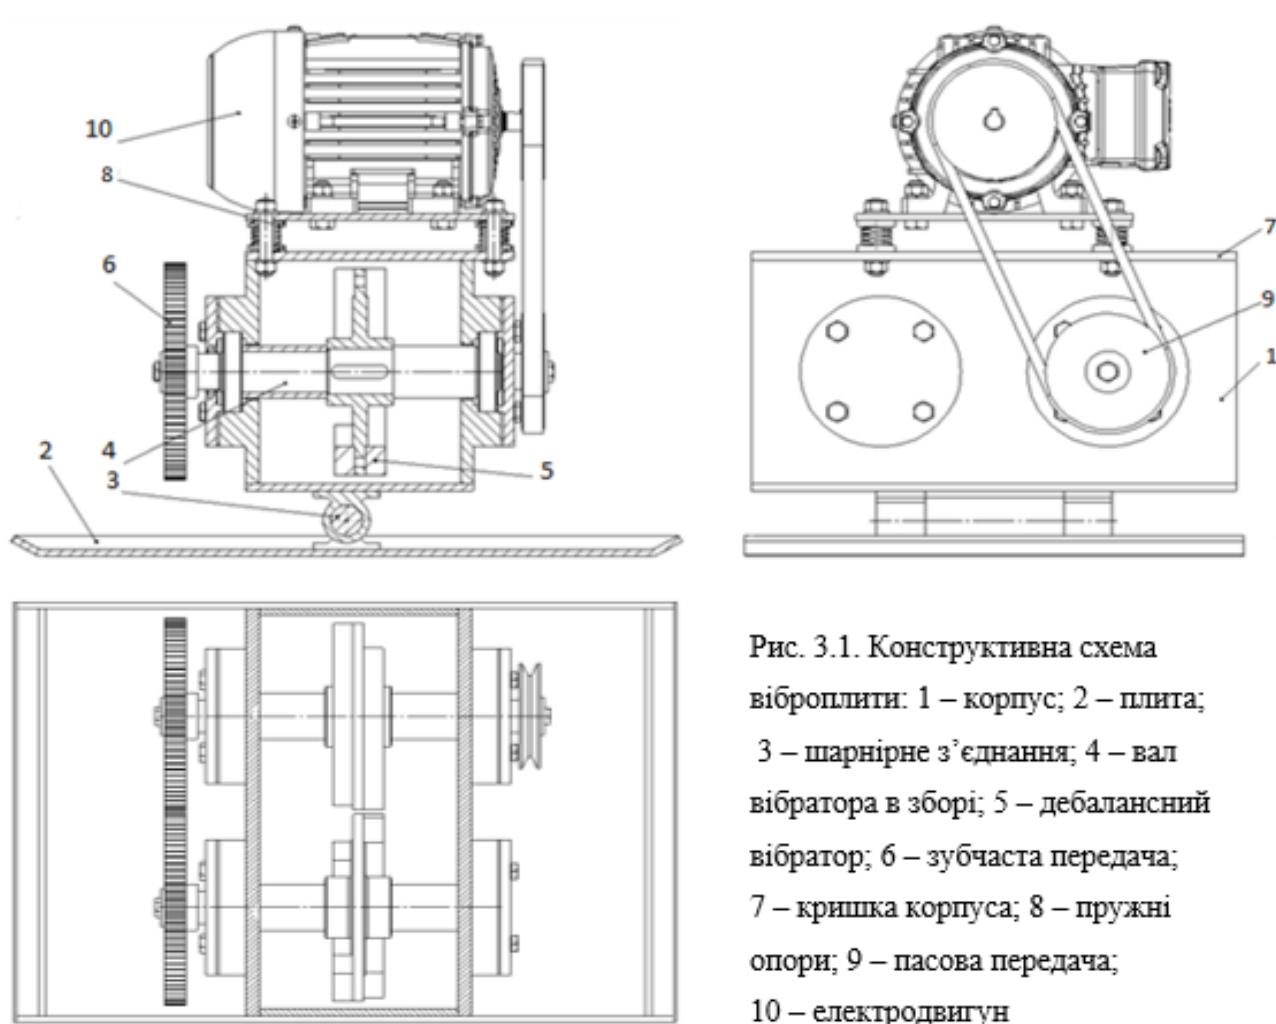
Конструктивна схема віброплити: 1 – корпус; 2 – плита; 3 – шарнірне з’єднання; 4 – вал вібратора в зборі; 5 – дебалансний вібратор; 6 – зубчаста передача; 7 – кришка корпуса; 8 – пружні опори; 9 – пасова передача; 10 – електродвигун
